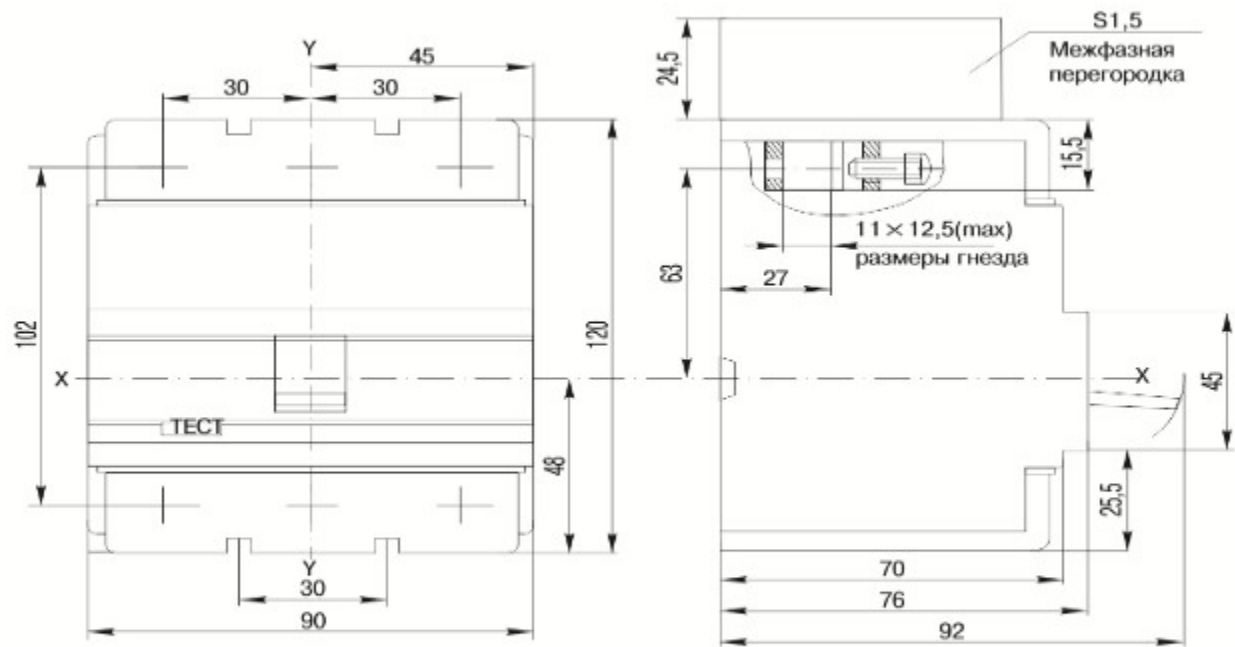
Габаритные и установочные размеры выключателя BA88-33
